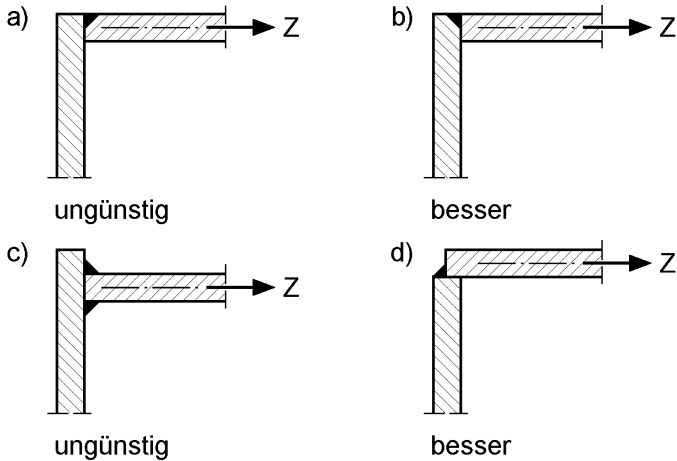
Bewertung von Anschlussdetails bezüglich der Terrassenbruchgefahr
